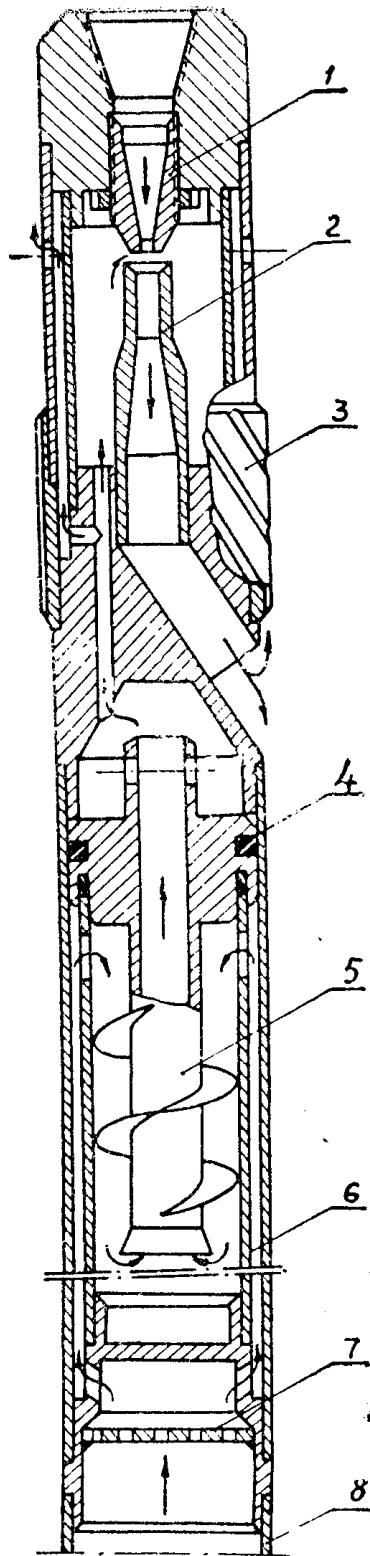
Эжекторный колонковый снаряд. 1 — посадка; 2 — смеситель; 3 — винтовой пакер; 4 — сальник; 5 — шнековый гидроциклонный шламоуловитель; 6 — шламовая труба; 7 — решетка; 8 — колонковая труба
